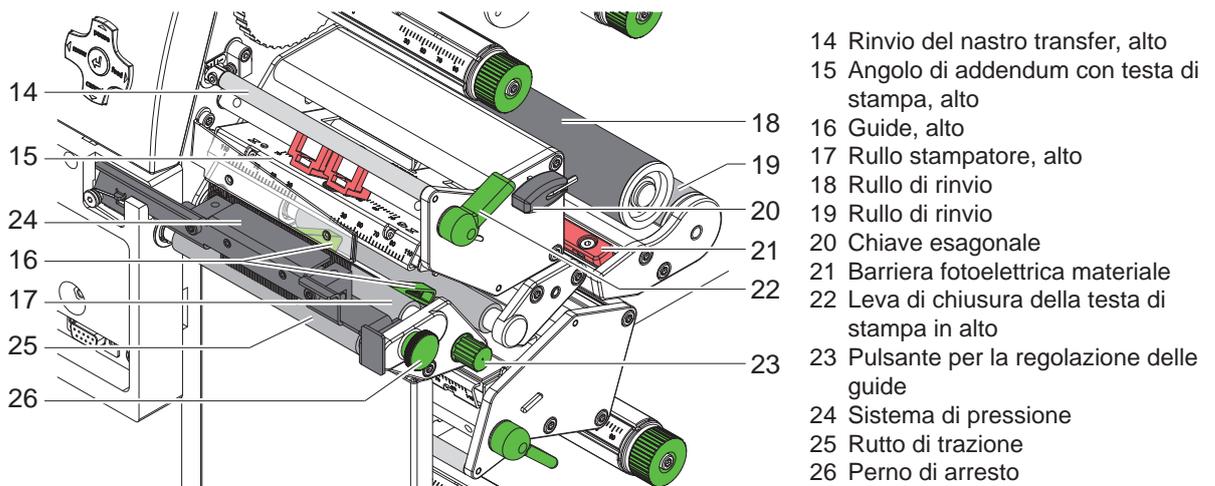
Meccanica di stampa - gruppo superiore stampante XD4T
